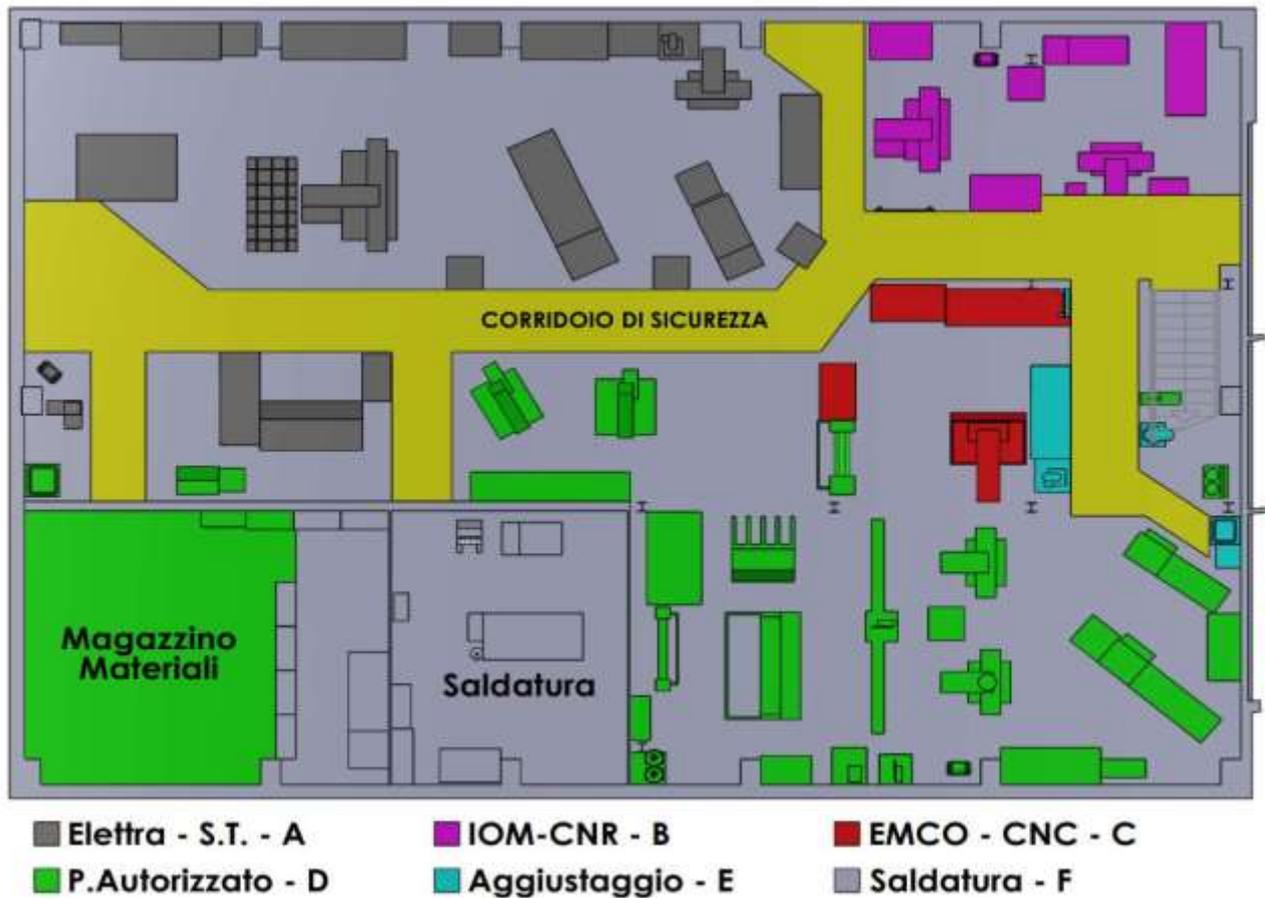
Planimetria dell'Officina con individuazione delle diverse aree
